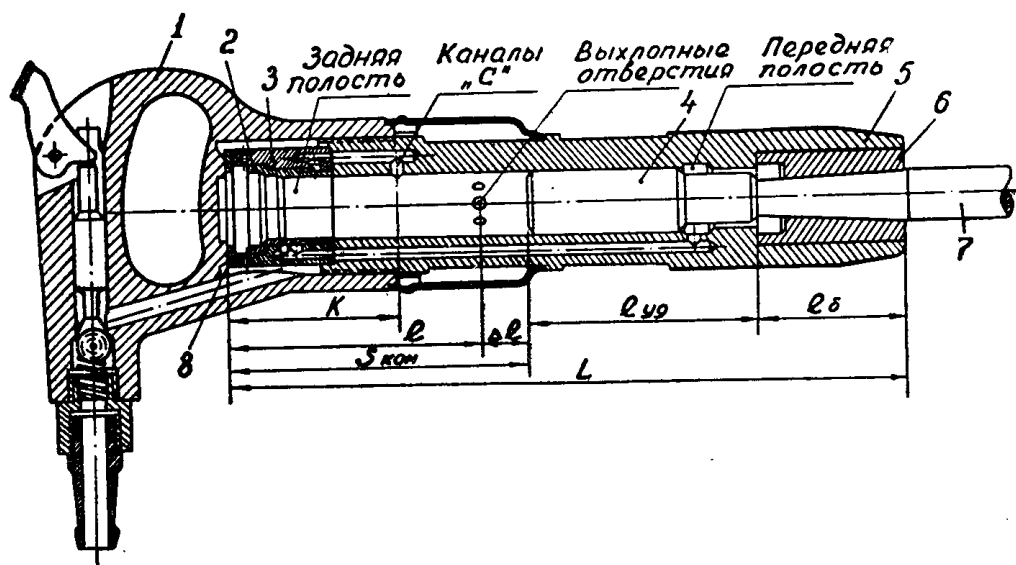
Клепальный молоток типа КЕ с конусной буксой: 1 — рукоятка; 2 — золотник; 3 — золотниковая коробка; 4 — ударник; 5 — ствол; 6 — направляющая букса; 7 — рабочий инструмент (зубило); 8 — промежуточное кольцо.
